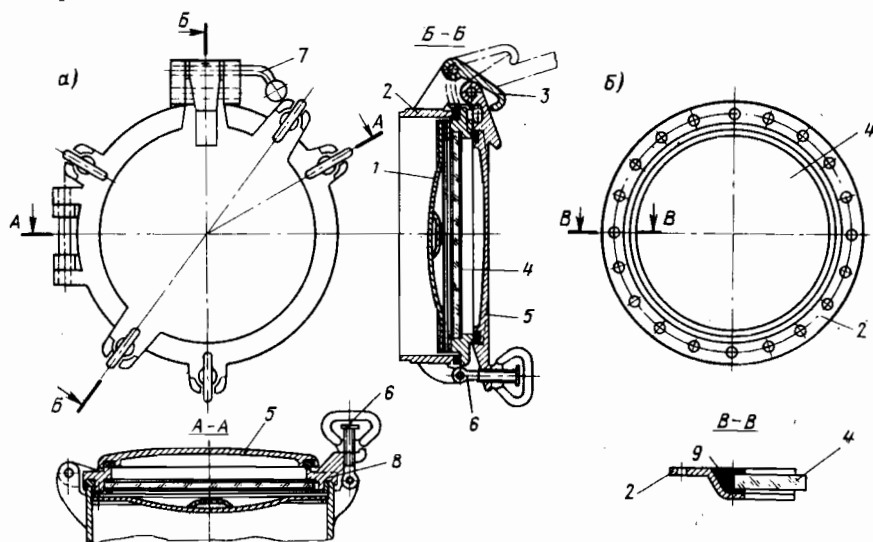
Иллюминатор бортовой: а — створчатый; б — глухой.
